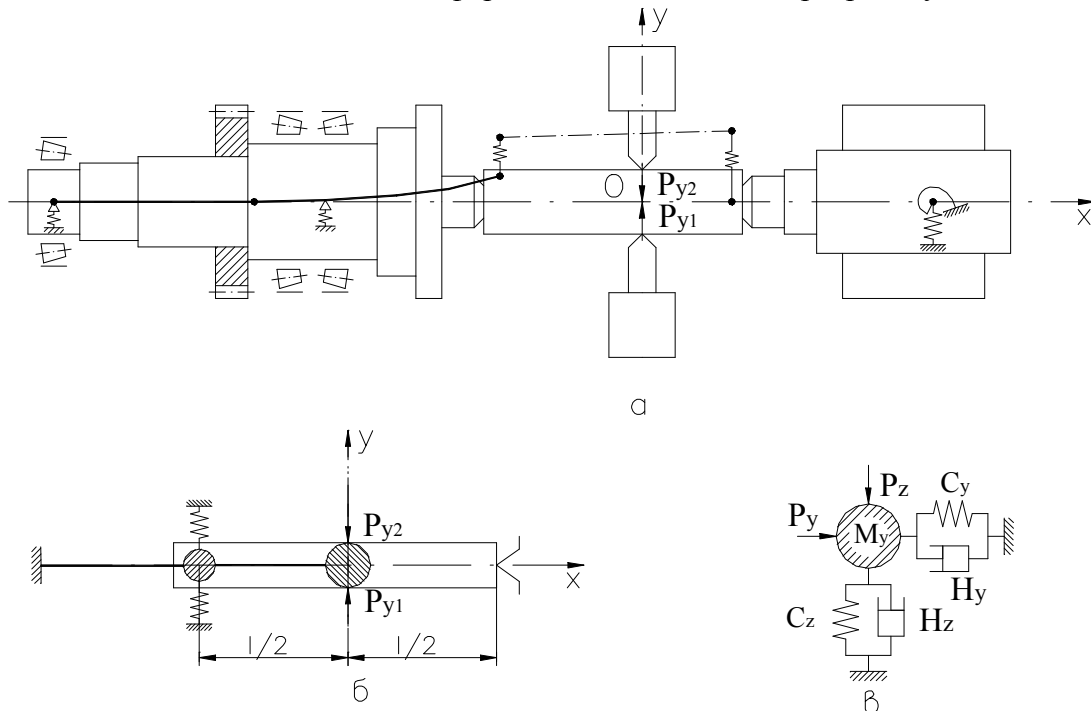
Розрахункова схема шпindelної групи токарного верстата:
